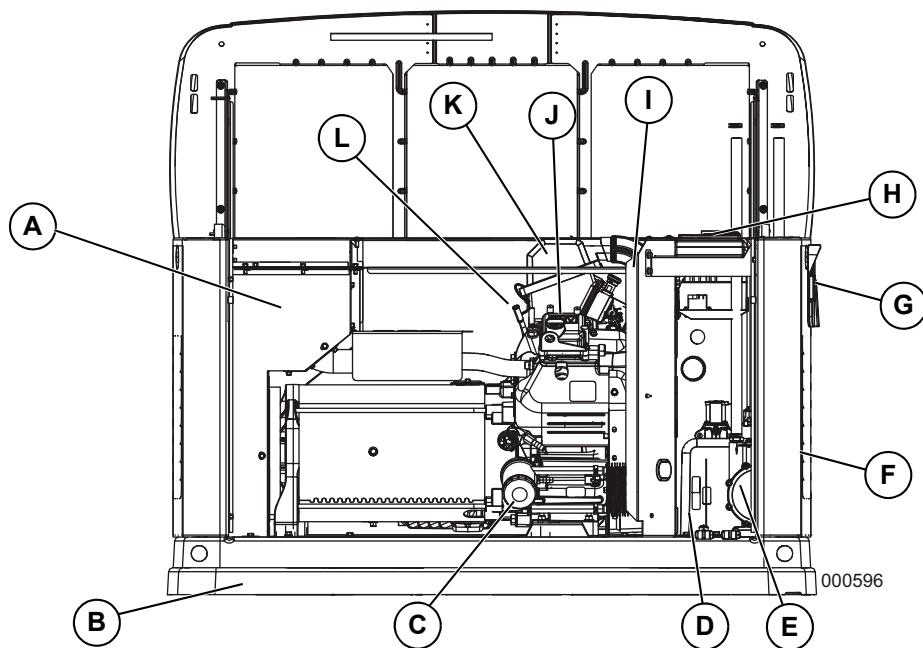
Двигатель GT-990, 10 и 13 кВА
